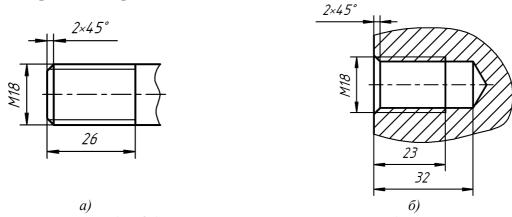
Обозначение размеров элементов с резьбой: a — на стержне; δ — в отверстии
